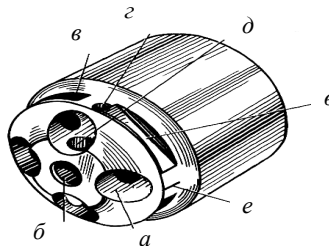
Корпус газового двигуна (вид спереду):
